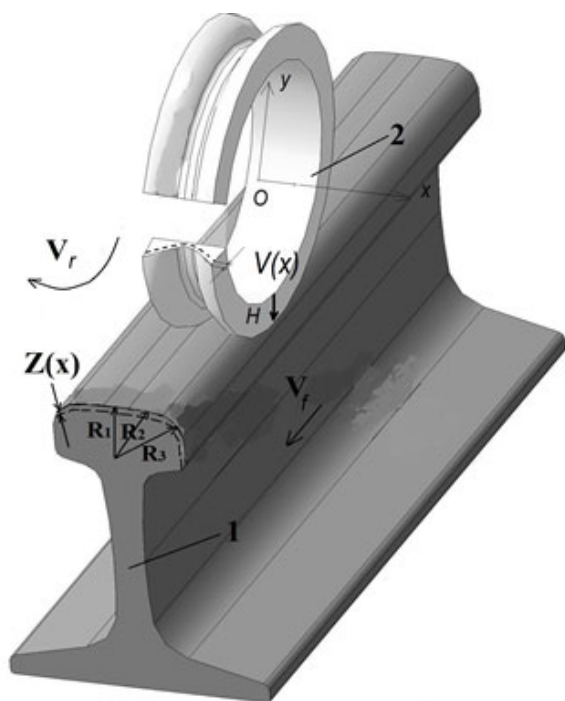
Существующая схема шлифования дорожки качения и рабочей поверхности головки рельса торцом абразивного круга: 1 – рельс; 2 – шлифовальный круг
